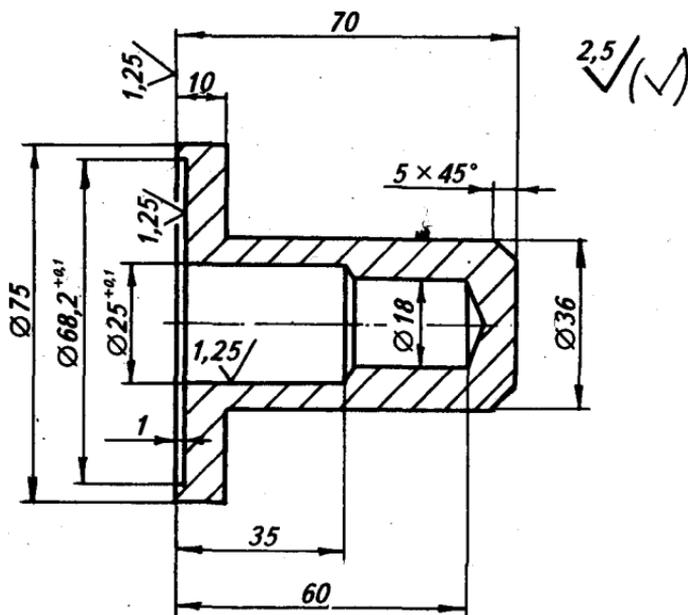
Оправка для запрессовывания сальника хвостовика.
